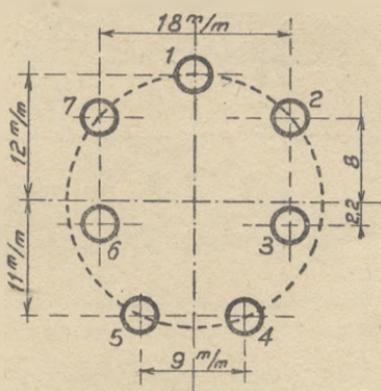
Vue par dessous du culot de la M. H. D 4 gécovalve : 1,3, plaques de diode; 4,5, filament; 6, cathode; 7, plaque de l'élément triode. La grille correspond à la borne du sommet de l'ampoule.
